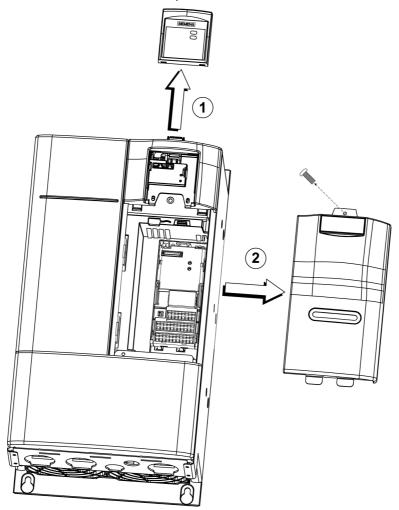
Desmontaje de las cubiertas en las construcciones D, E, F
